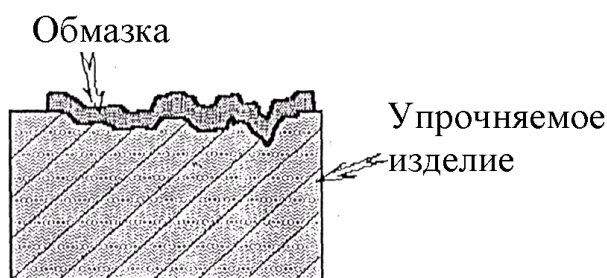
Схема нанесения обмазки на поверхность изделия
